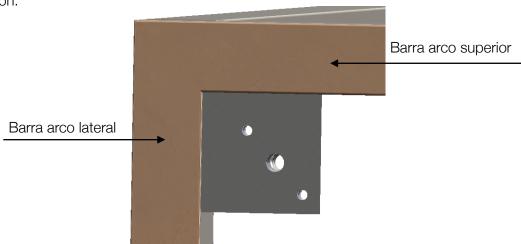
Detalle chapa soldada a la estructura. Fuente: elaboración propia.
